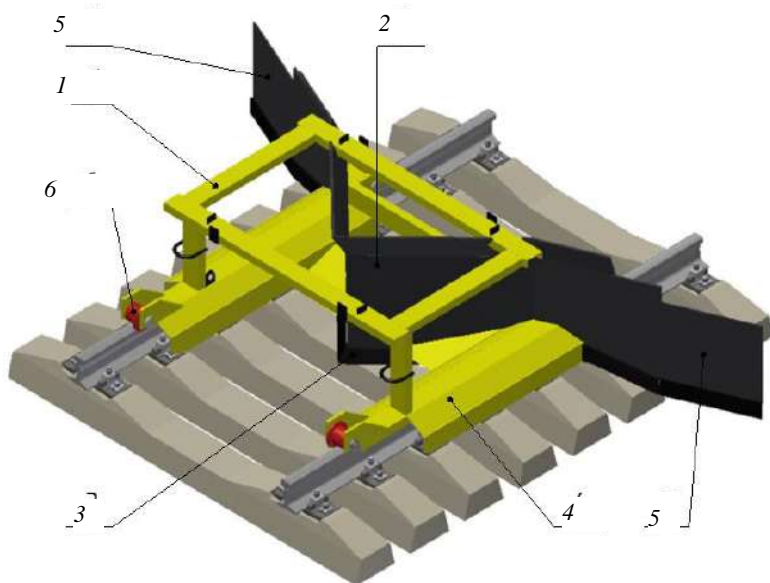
Конструкция устройства для перераспределения и планировки щебеночного балласта:
